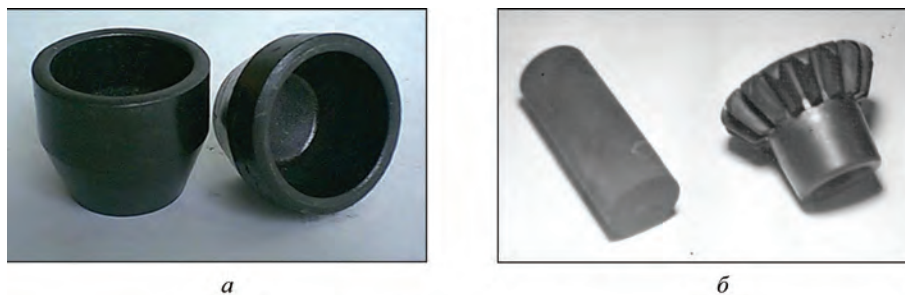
Примеры грамотного выбора схемы и температурно-силовых условий пластического деформирования высокопрочного чугуна: *a* – получение детали «корпус патрона электродрели» для Оршанского инструментального завода (Беларусь) штамповкой из цельной цилиндрической заготовки за один удар [33]; *б* – получение в несколько переходов заготовки конической шестерни (с зубчатым венцом) гидравлического насоса для фирмы «Хидравлика» (Болгария) [42]
